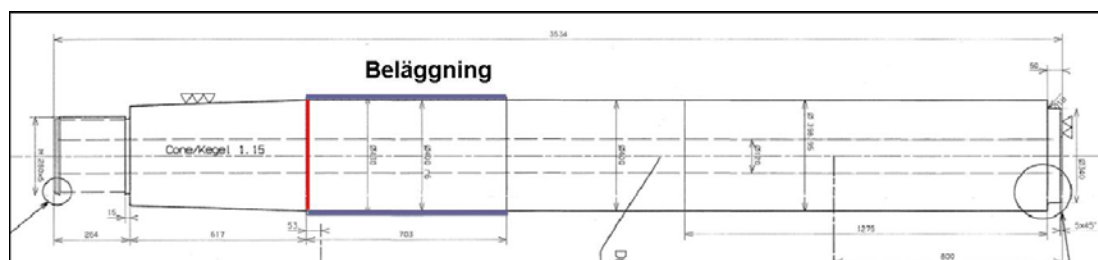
Roderaxeln. Beläggningen är tillverkad av rostfritt stål är visad med blågrått. Ett 120 millimeters hål i diameter har borrarats genom roderaxeln för Jastram-rotorns hydraulikrör. Stället där SB-roderaxel gick av har indikerats med rött.
